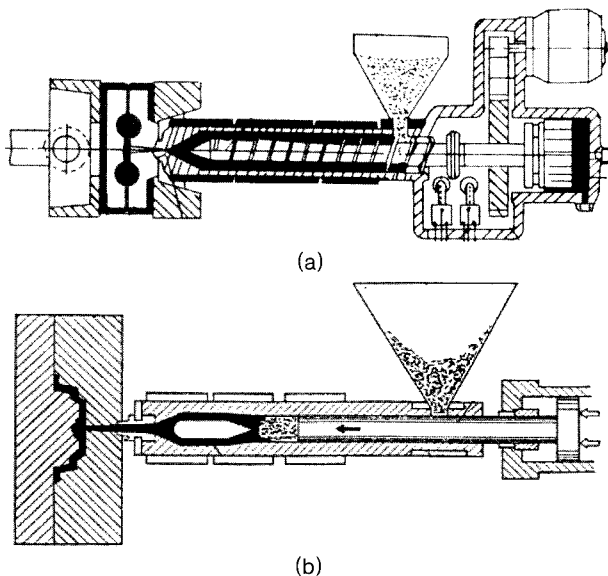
Difference of injection units in a conventional injection molding machine: (a) screw; (b) plunger types.
